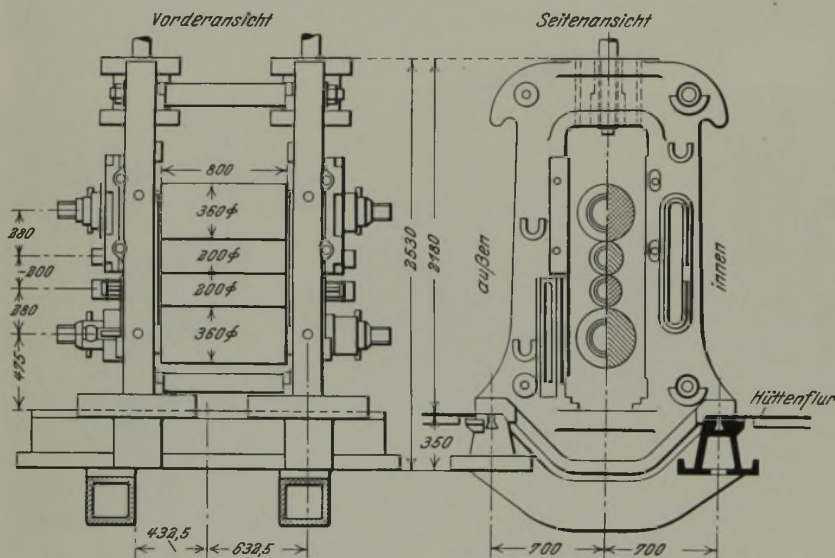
Vierwalzeinbau des Versuchswalzwerks mit SKF-Rollenlagern.
